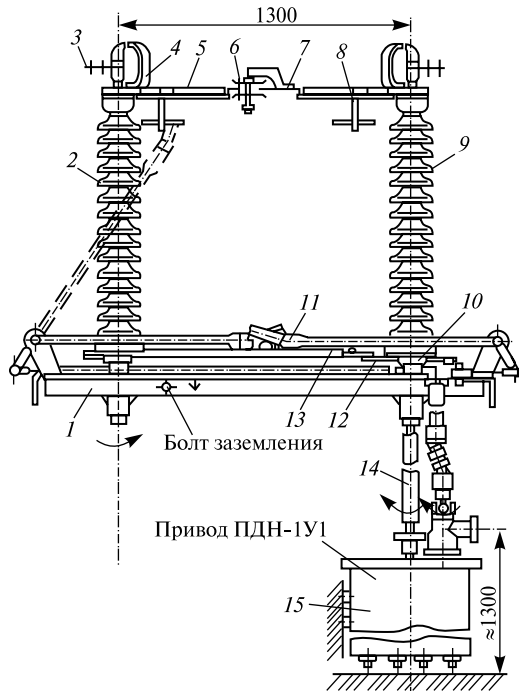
Разъединитель РНДЗ-2-110 с приводом типа ПДН-1
